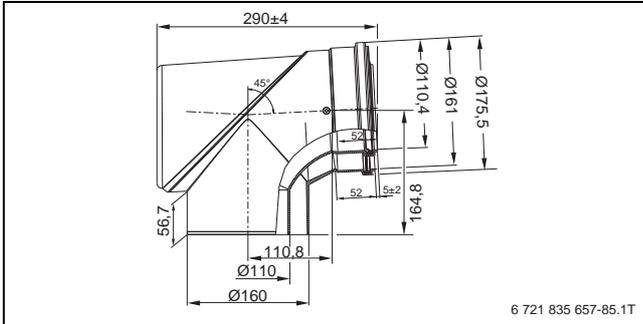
Konzentrisches T-Stück mit Prüföffnung Ø 110/160 (Maße in mm)
